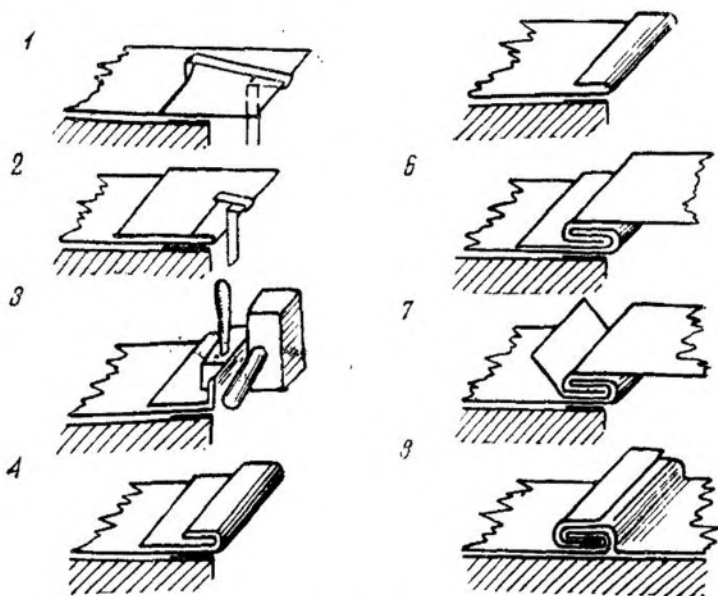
Заготовка полуторного фальца по способу Л. А. Лапшова
